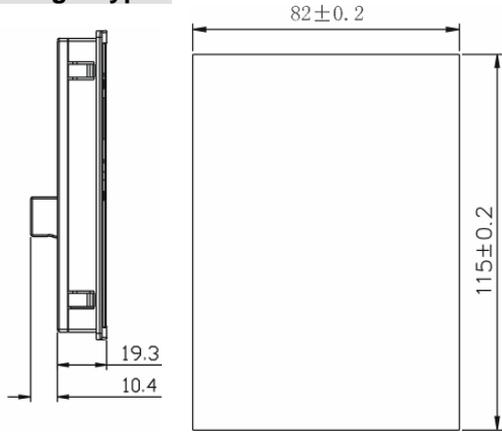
Dimension of small keypad. Hình A-11 installation of small keypad
